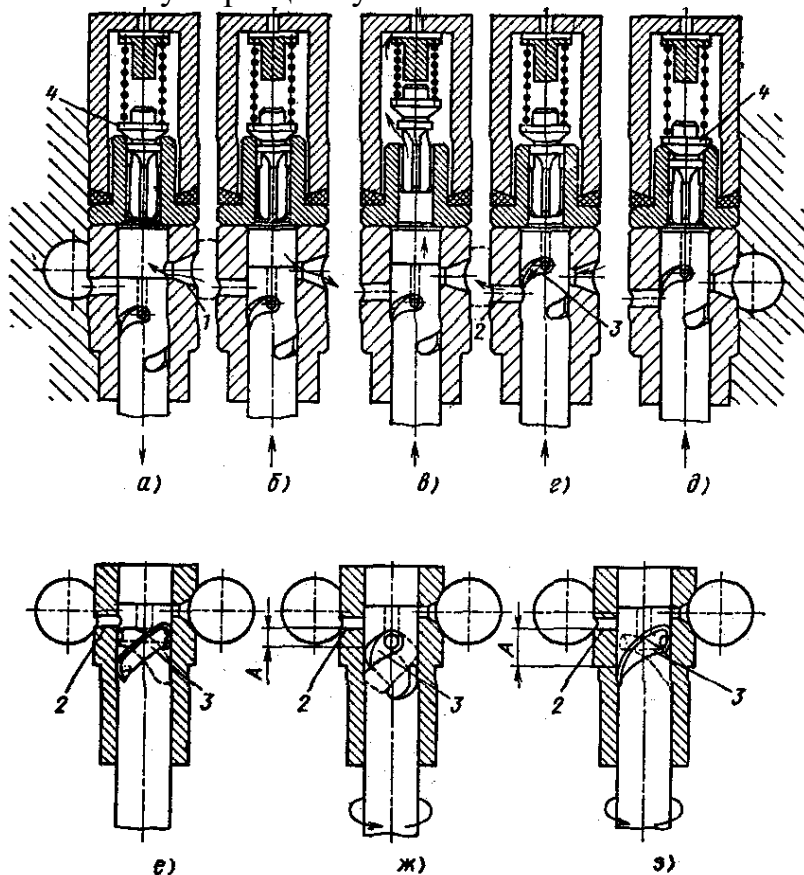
Схеми роботи плунжерної пари нагнітального клапана: 1 – впускний отвір; 2 – перепускний отвір; 3 – гвинтовий паз; 4 – нагнітальний клапан.
